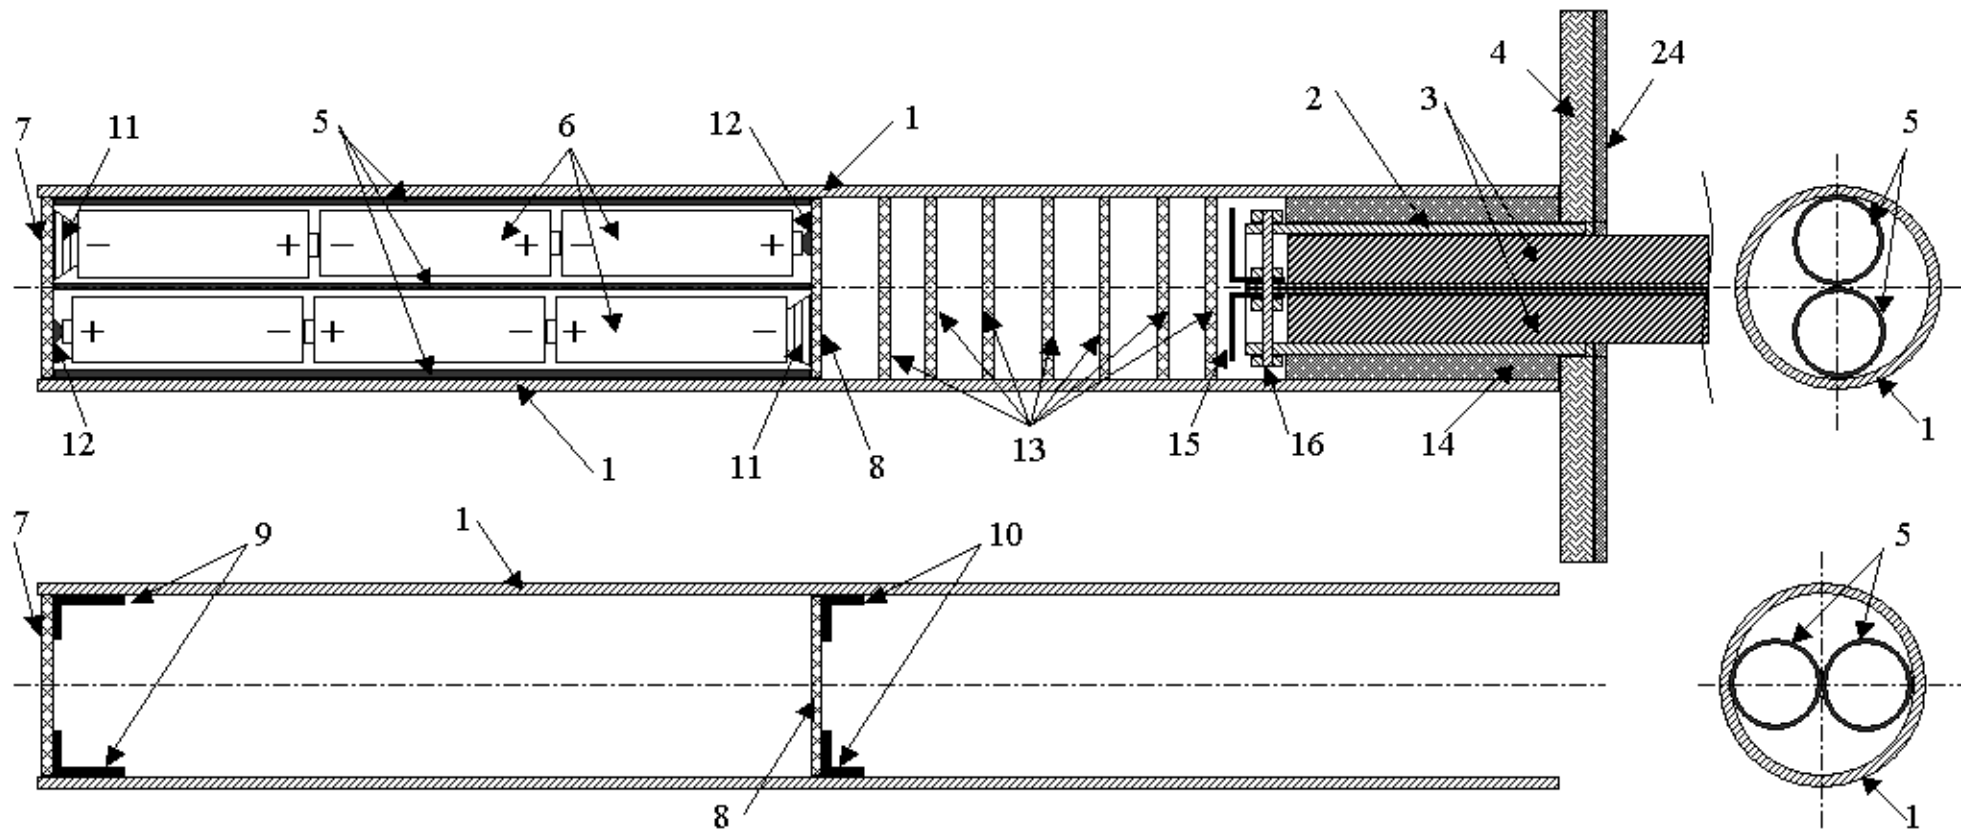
Схема конструкции эфеса светового меча и крепления лезвия.
